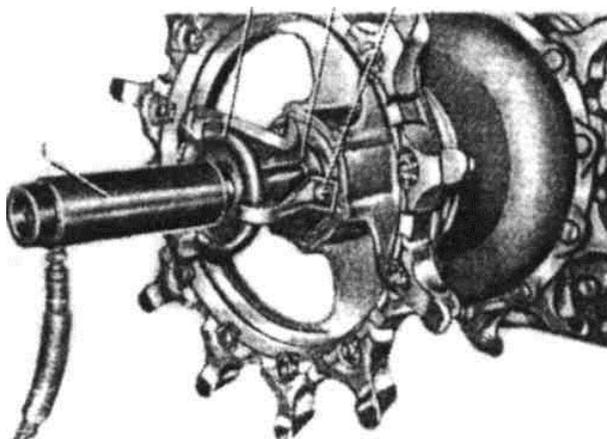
Установка приспособления УК-1С6Б для спрессовки ведущего колеса танка Т-72 и машин на его базе с использованием гидравлического пресса ПГ-20М
